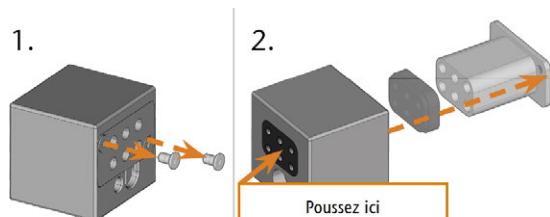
RETIRER UN INSERT D'UN MAGASIN D'OUTILS
